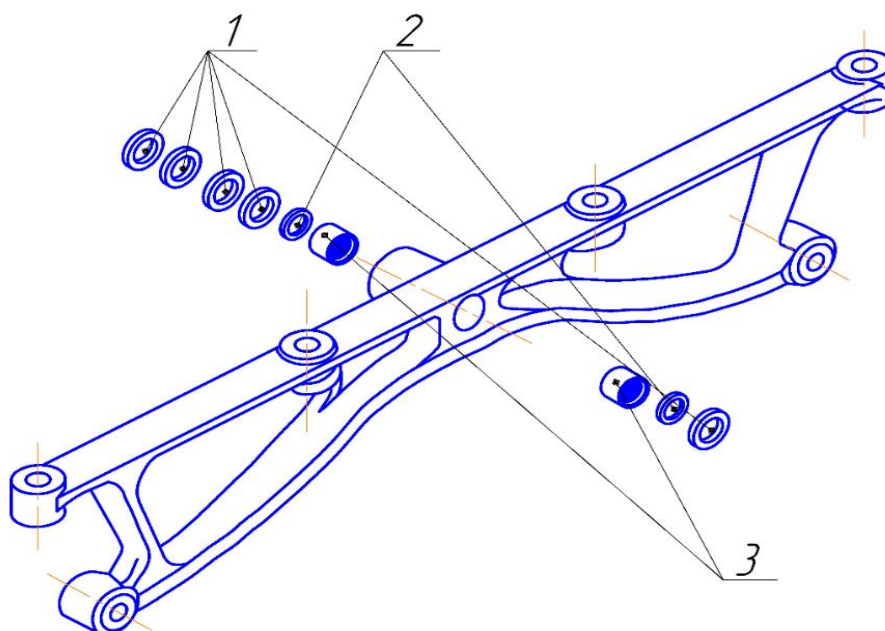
Конструкція підвісного пристрою базової машини:
